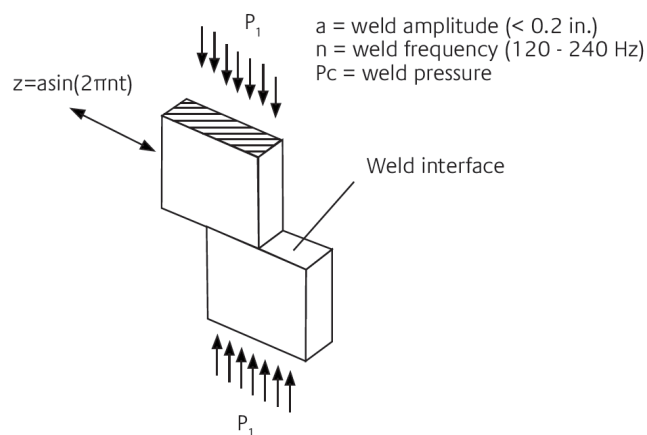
Rappresentazione schematica del processo "vibration welding"
